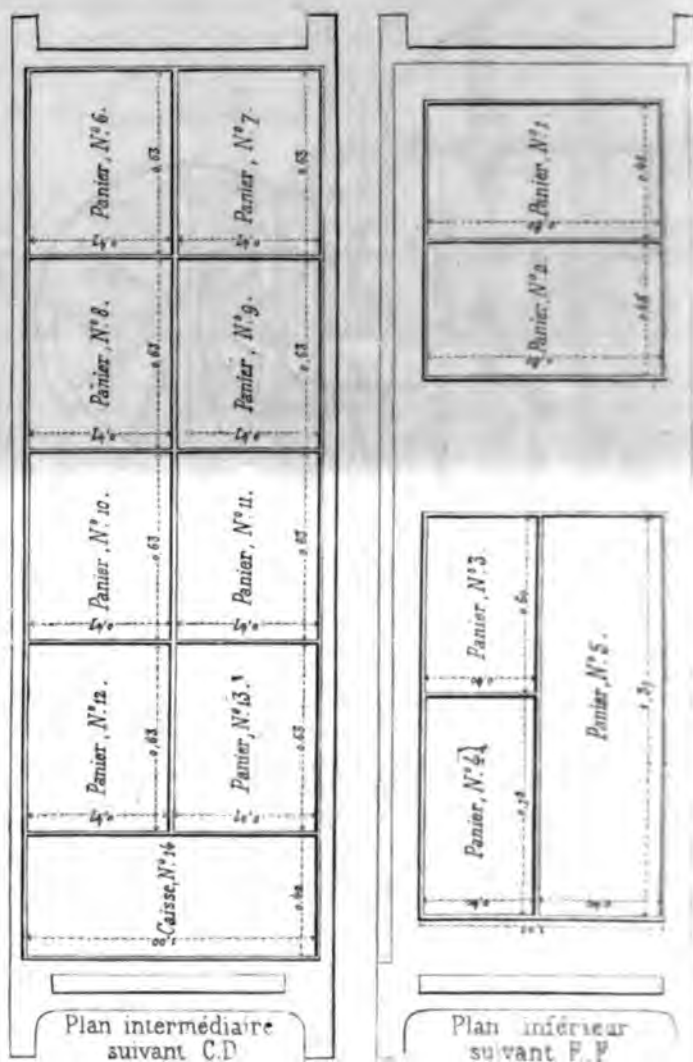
FIGURE CXX. — Plan figuratif du caisson d'ambulance. (Mortier & 20 août 1854.)
